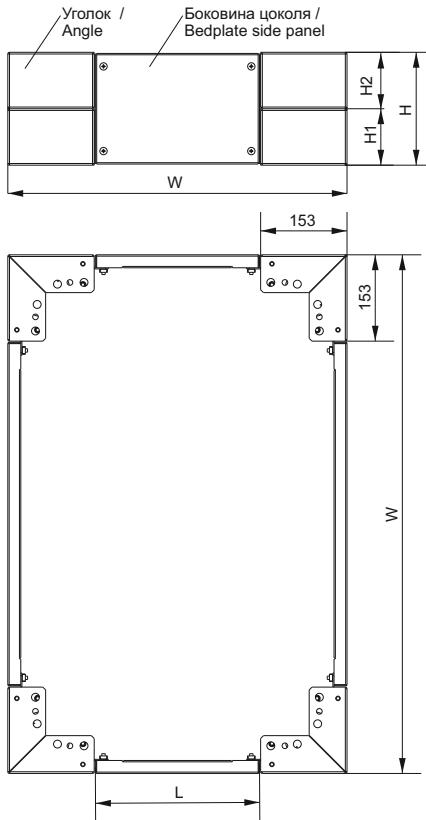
Цоколь в сборе / Figure 1 – Bedplate assembly
